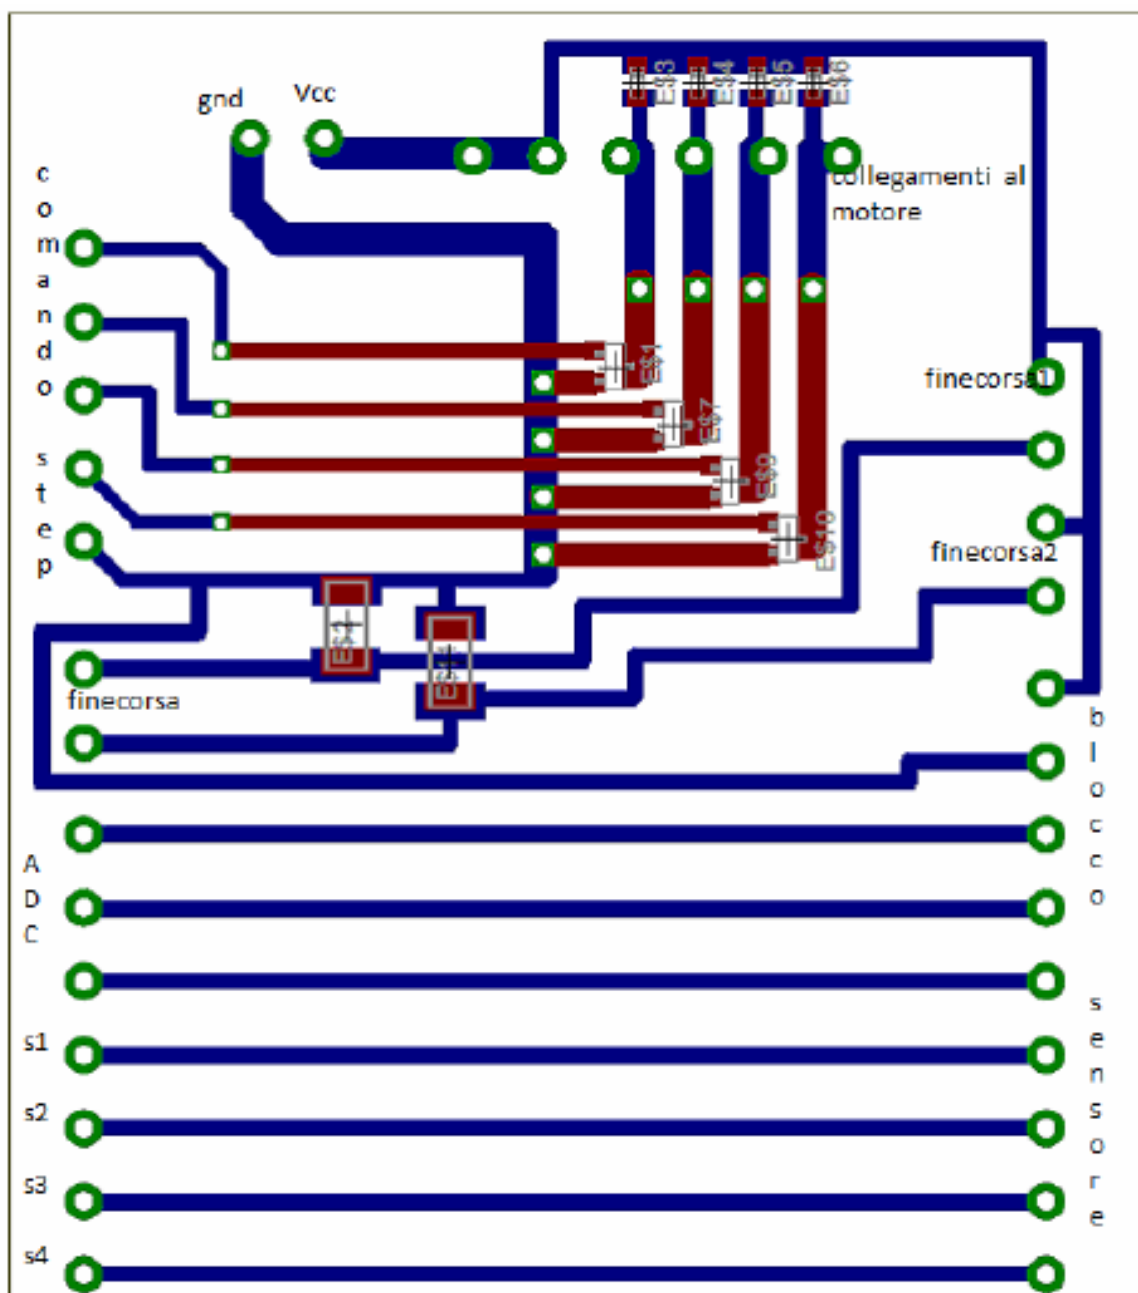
Circuito elettrico stampato del pcb principale: prima versione
